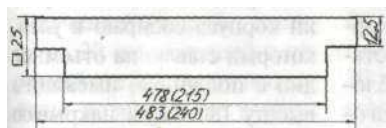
Верхние и нижние бруски боковой стенки корпуса (в скобках — размеры боковых брусков)
